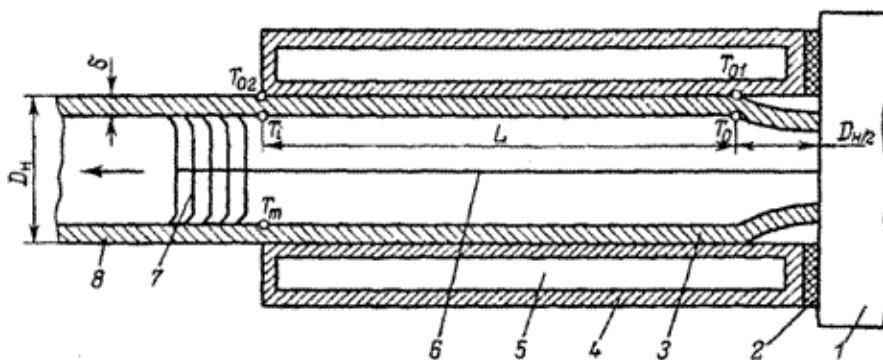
Схема калибрующего устройства с применением внутреннего давления (калибровка трубы по наружному диаметру):
